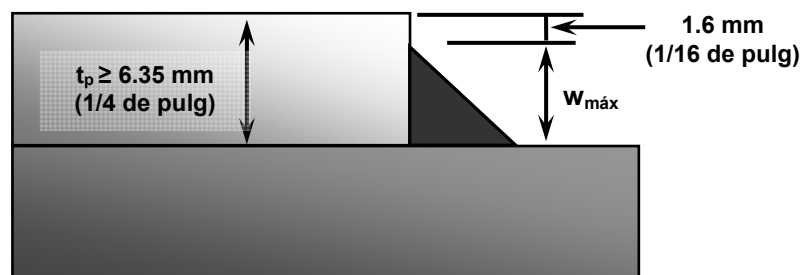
Tamaño máximo de la soldadura de filete.
